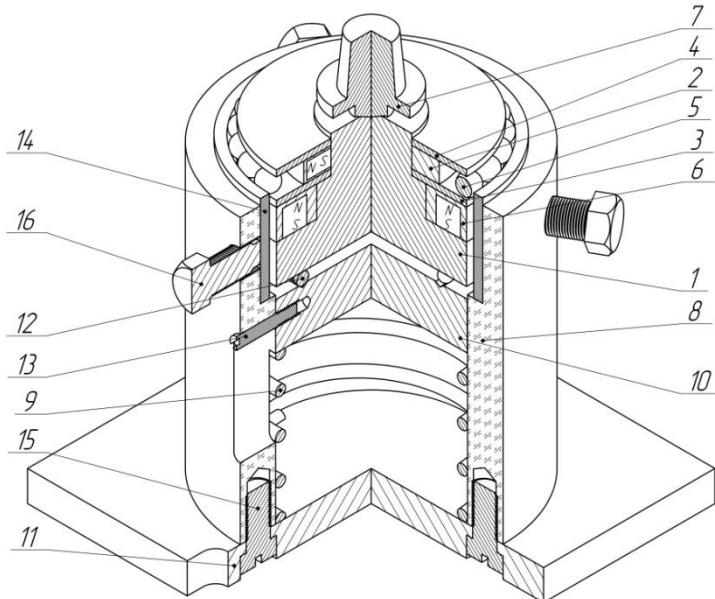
Конструкция устройства для отделочно-упрочняющей обработки:
